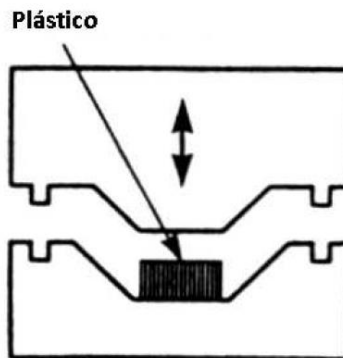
Esquema del moldeo por compresión (Díaz, F., 2012).
